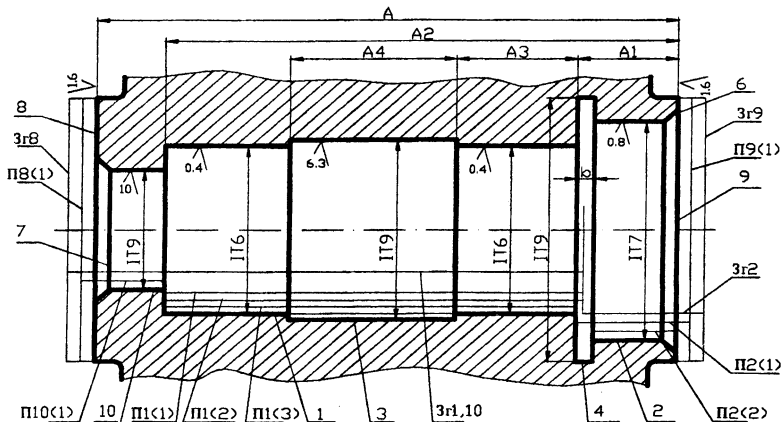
ФМ образующий вспомогательную сборочную базу и схема снятия припуска. Зг — заготовка, П_i(j) — j-ый припуск, i-ой поверхности
